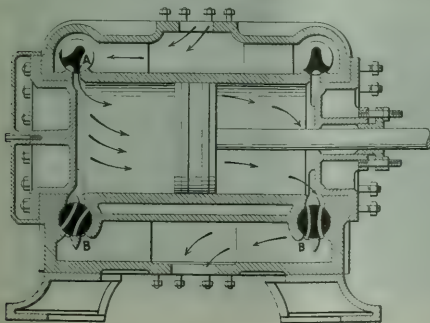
CILINDRO DE UNA MÁQUINA DE VAPOR
